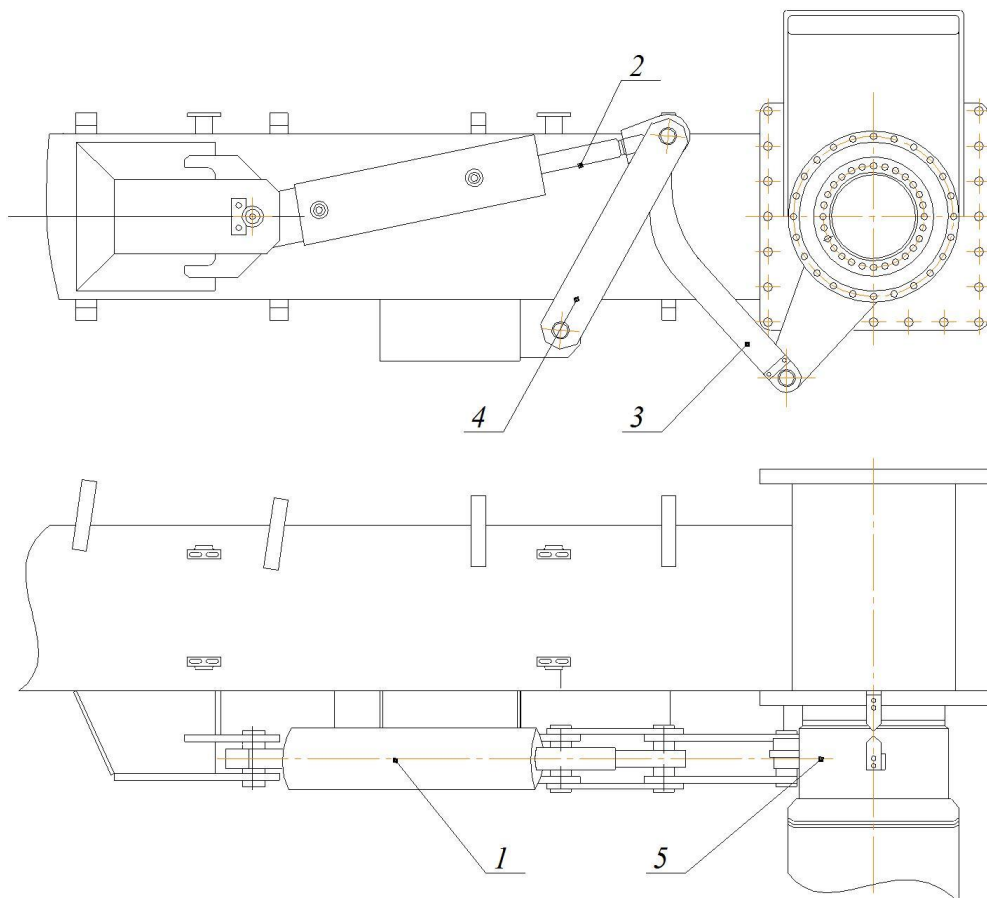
Механизма поворота: 1 – гидрацилиндр; 2 – шток; 3 – ведущая рейка; 4 – планка; 5 – поворотная колонна
